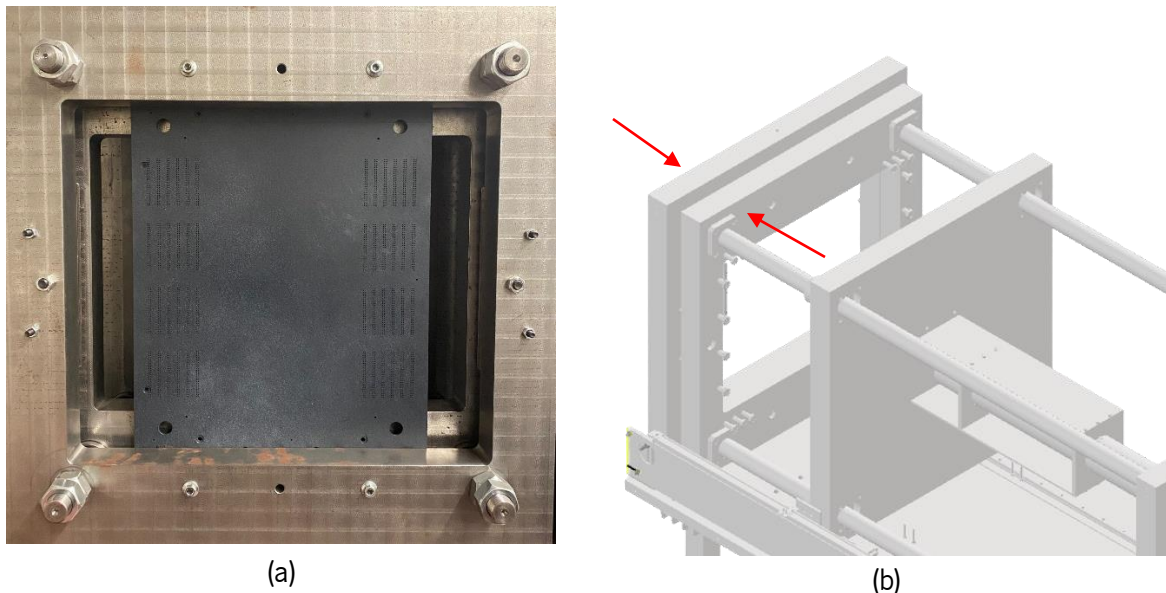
(a) Imagem da fixação da placa de cama de agulhas na máquina-ferramenta. (b) Ilustração do local em que a placa está a ser fixa na máquina.
